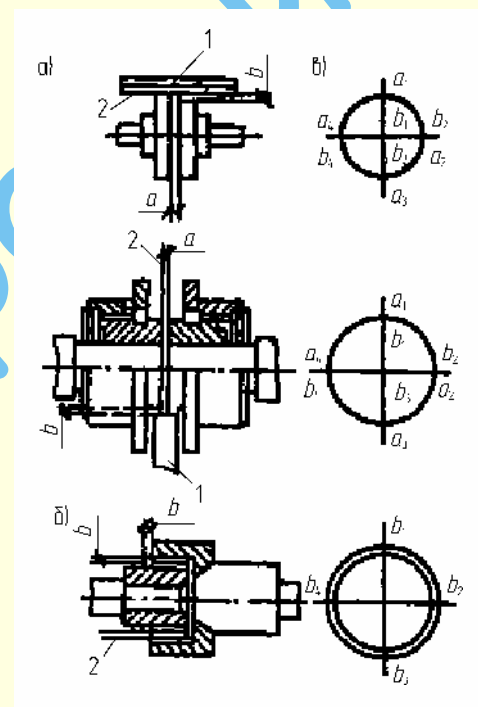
Установка муфты с помощью линейки и щупа:
